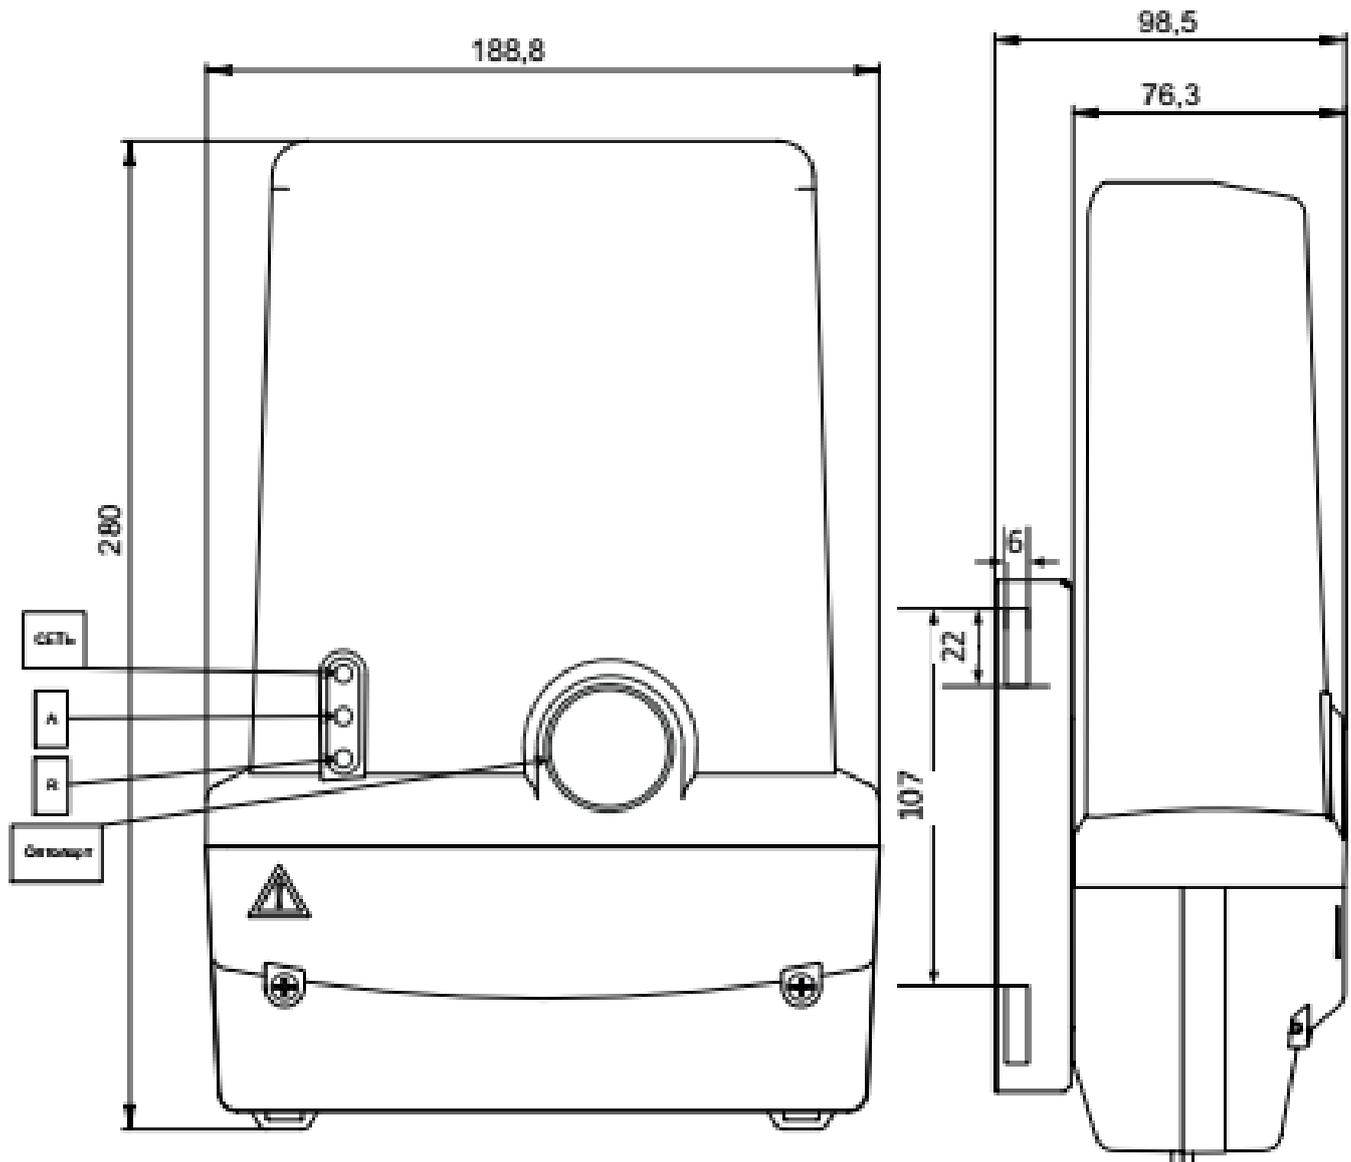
Габаритные размеры счетчика в корпусе «С36»
